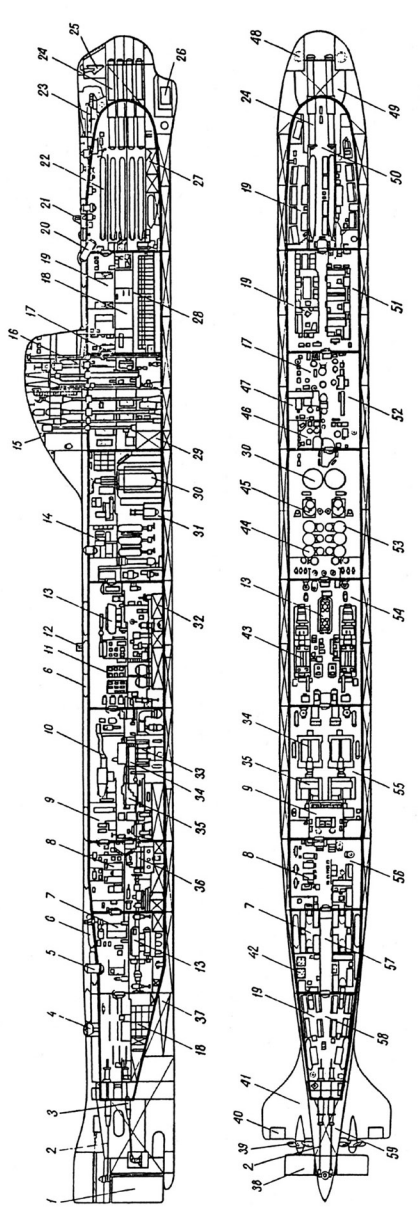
原子力潜水艦プロジェクト 645 型 縦断面図と水平断面図
